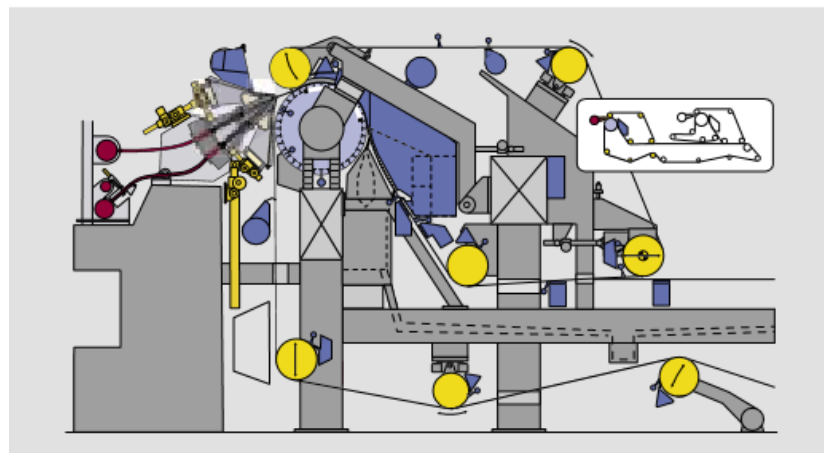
Схема DuoFormer™ Base та приклад встановлення додаткового формера
